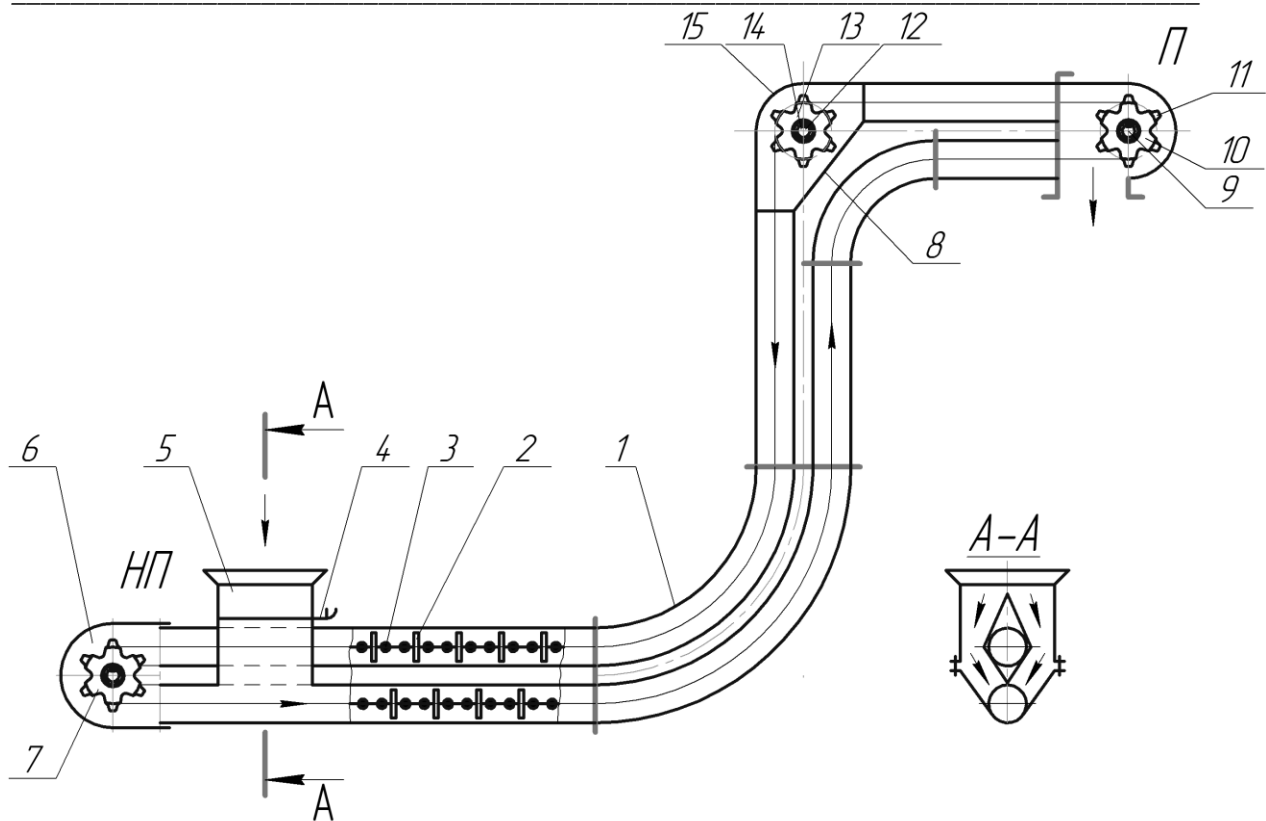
Гнучкий трубчастий конвеєр з вертикальною подачею сипких матеріалів : 1-труба; 2- круглі диски; 3- гнучкий ланцюг; 4- шибер; 5- бункер; 6- радіусний кут; 7- натяжна зірка; 8-коса півкругла поверхня; 9- вал приводної зірочки; 10- приводна зірочка; 11- зуби; 12- вал паразитної зірочки; 13- зуби паразитної зірочки; 14- паразитна зірочка; 15- верхній радіусний кут.
